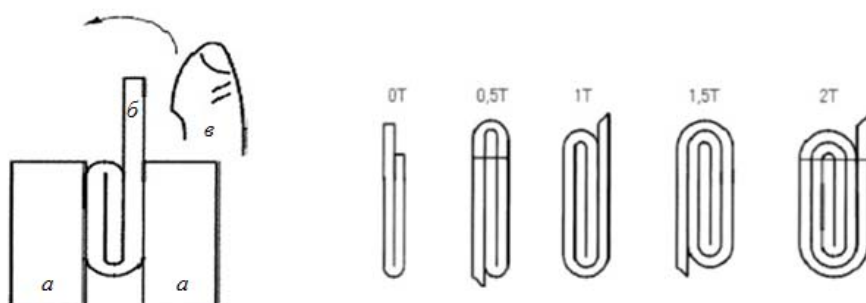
Испытание на изгиб: а – тиски; б – образец; в – палец
